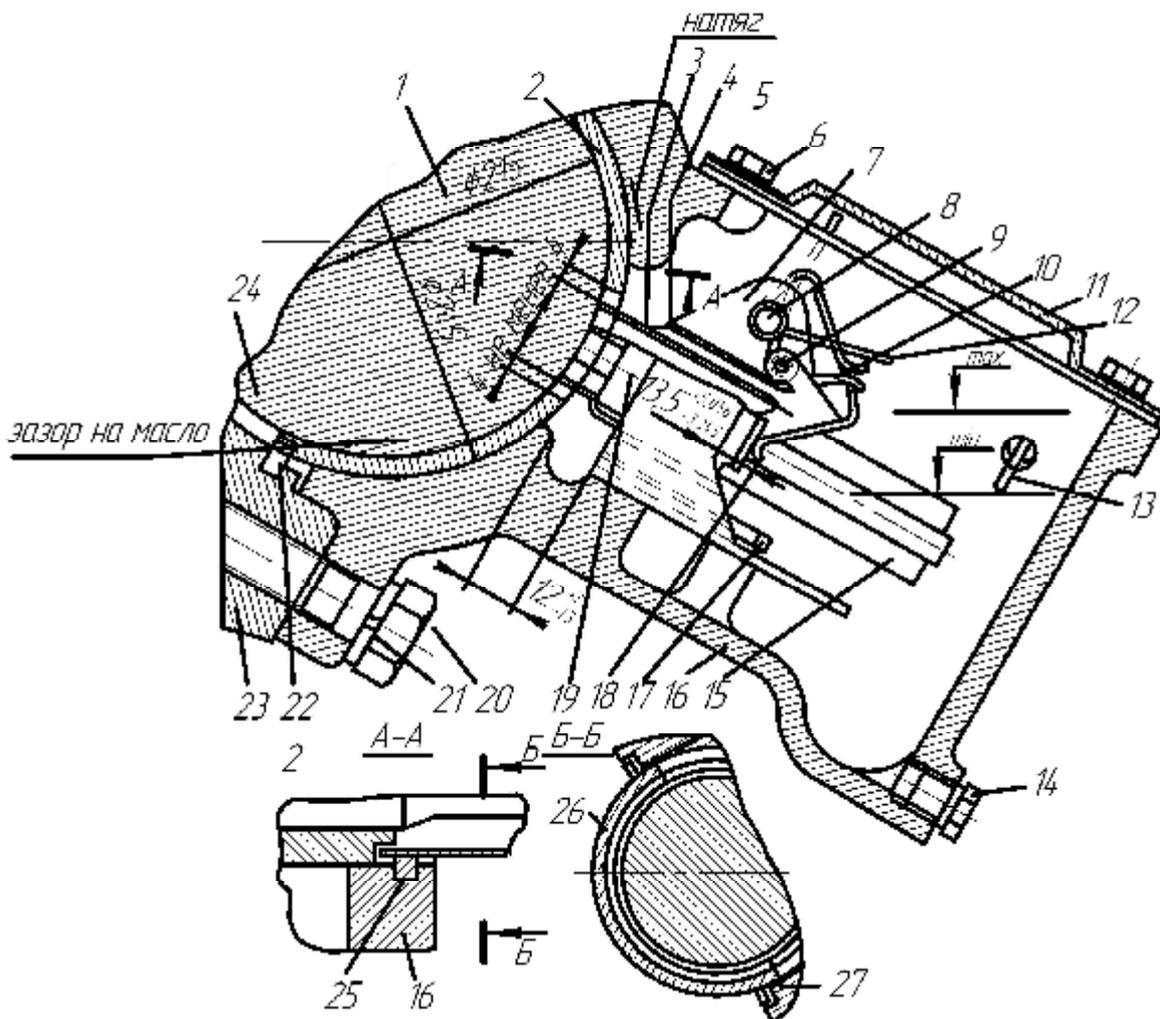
Измерение зазора «на масло» в МОП: 1 – ось колесной пары; 2, 24 – вкладыши нижний и верхний; 3 – пружина пластинчатая; 4 – направляющая корпуса; 5 – прокладка; 6, 17, 20 – болты; 7 – корпус полистера; 8 – стержень; 9 – ось рычага; 10 – пружина; 11, 27 – крышка; 12 – фиксатор пружинный; 13 – масломер; 14 – пробка сливная; 15 – пакет фитилей; 16 – корпус подшипника; 18 – рычаг; 19 – коробка пакета фитилей; 21 – шайба; 22 – шпонка; 23 – остов тягового двигателя; 25 – шнур уплотнительный; 26 – уплотнение; 28 – скоба
